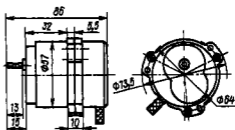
19 Габаритные и установочные размеры двигателей ДСР
